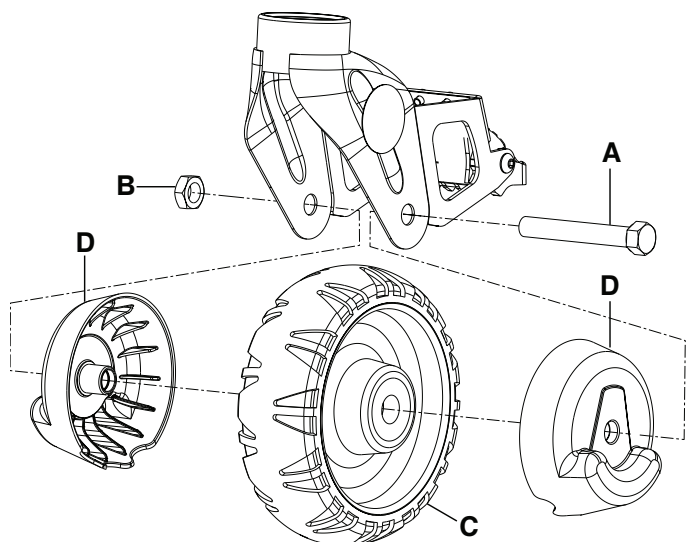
Rodas de maca com protecções de rodas, com travões de roda
